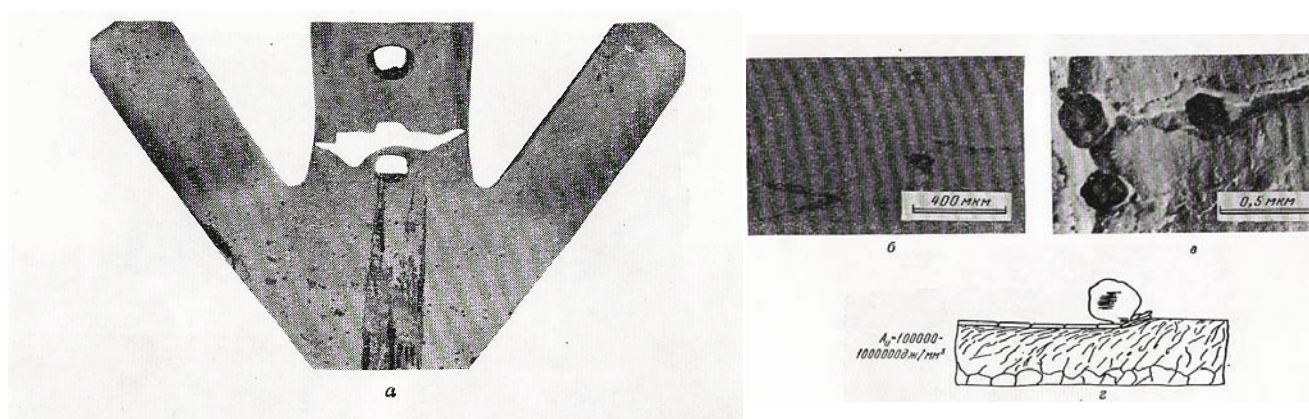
Механо – хімічна форма абразивного зношування лапи культиватора:
